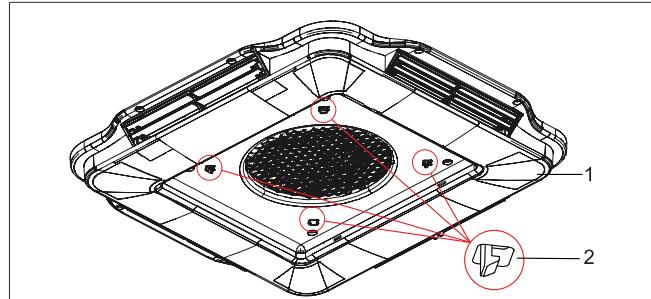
Conexión del conjunto de distribuidor de aire al soporte de montaje
